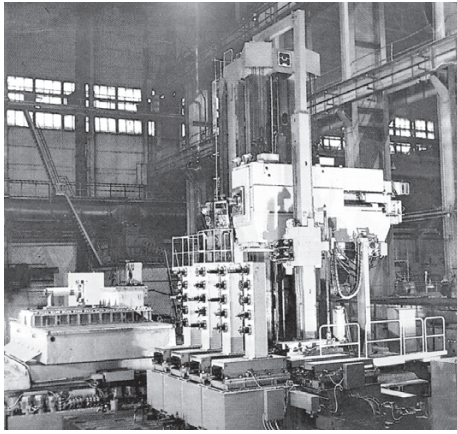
Тяжелый многоцелевой станок сверлильно-фрезерно-расточной группы с поворотным-подвижным столом для обработки корпусных деталей массой до 200 т
